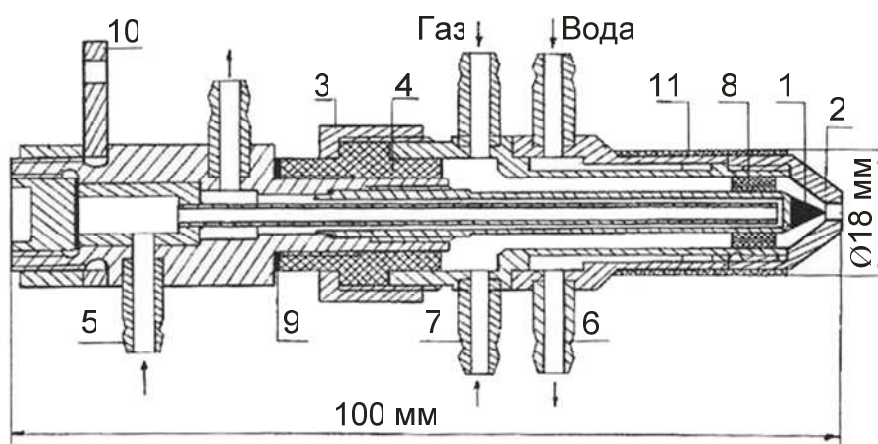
Плазмотрон для сварки изделий на обратной полярности:
